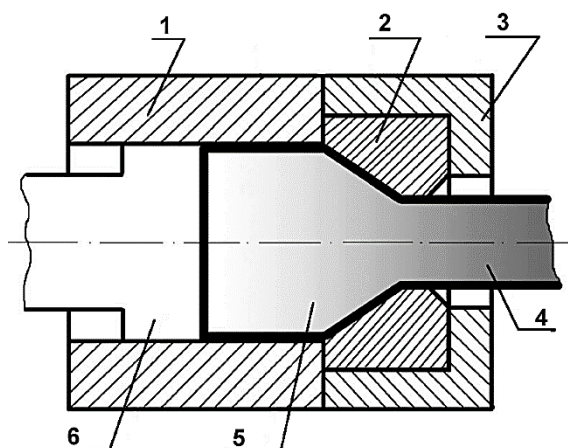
Технологическая схема экструзии: 1 – контейнер пресса; 2 – матрица; 3 – обойма; 4,5 – экструдированная заготовка; 6 – плунжер пресса
